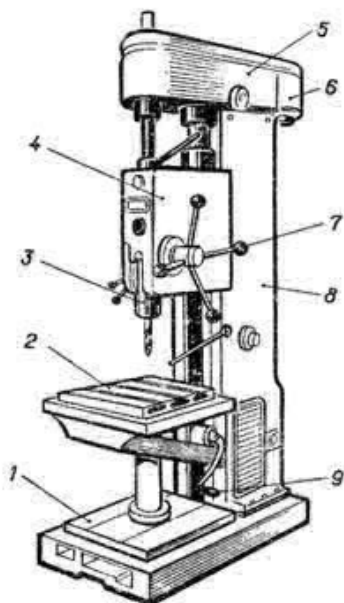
Розташування складових частин свердлильного верстата 2А135
